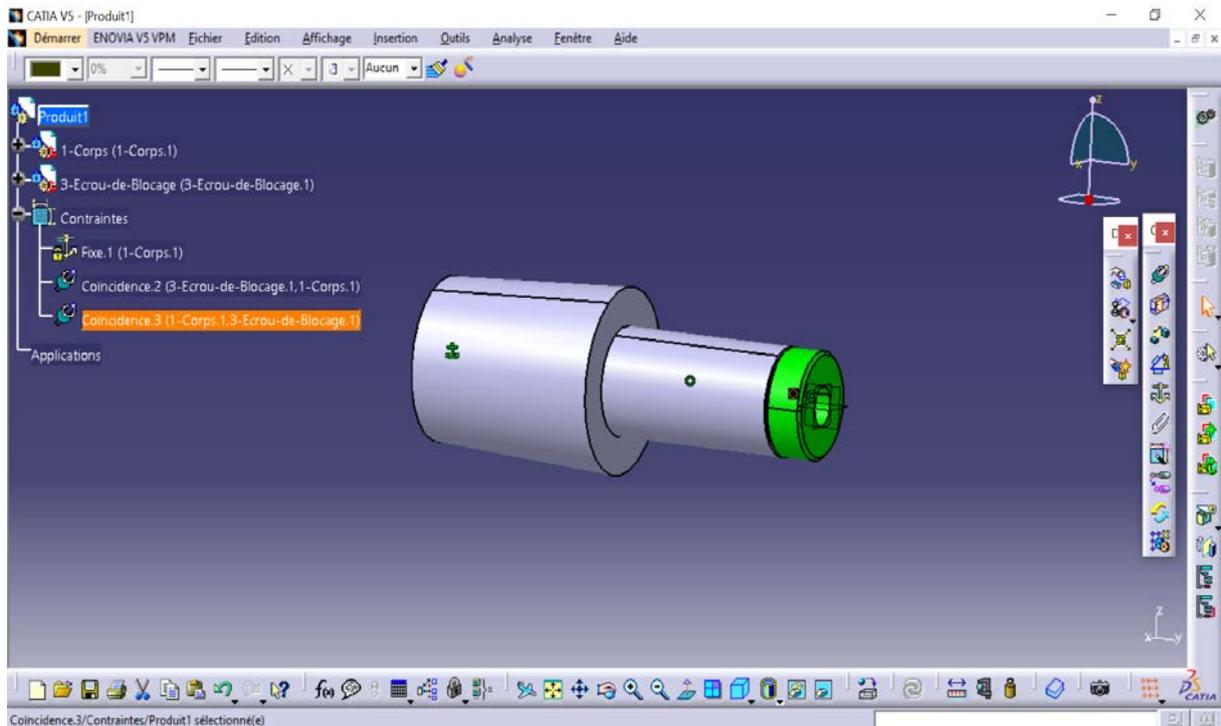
Assembly Design des Pièces 1 et 3 [1], [2]
